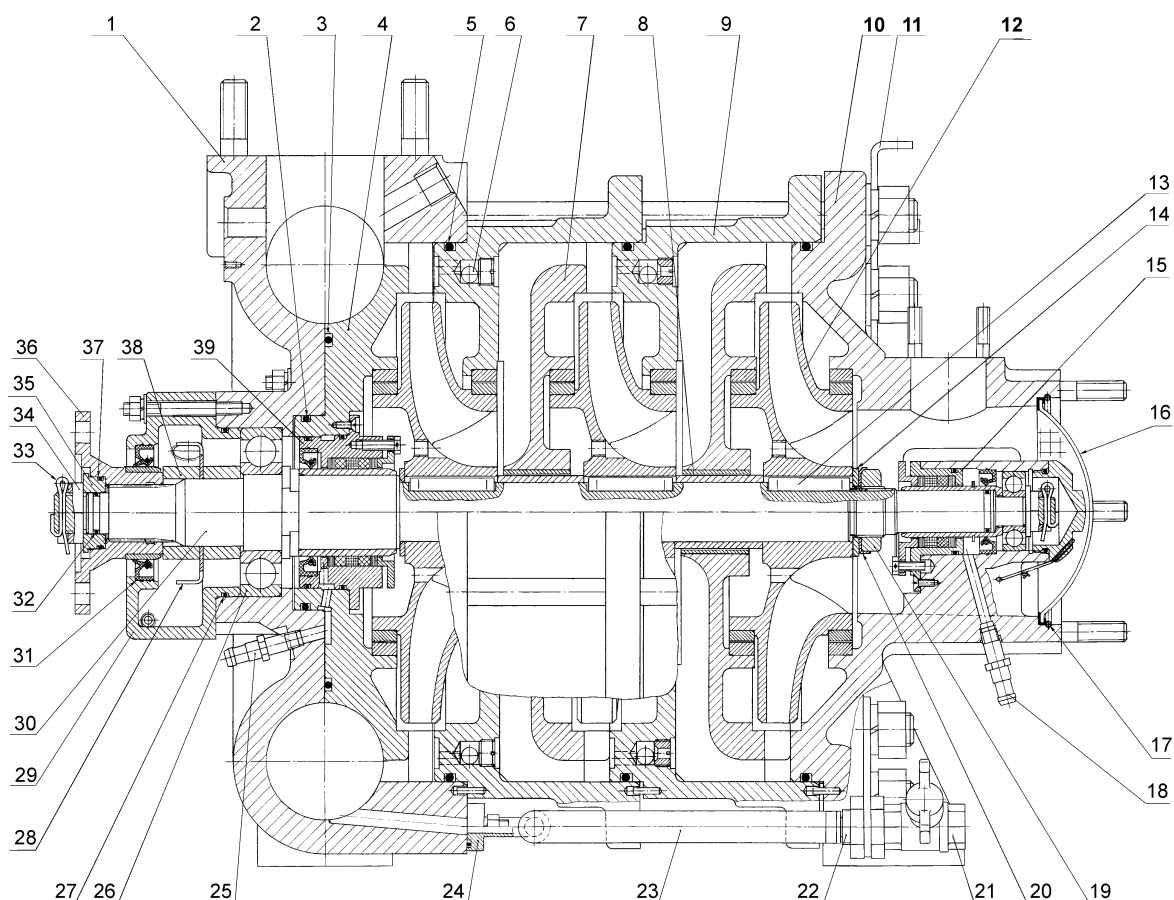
Насос центробежный (разрез по оси ротора): 1 – корпус; 4 – аппарат направляющий третьей ступени; 6 – клапан; 7 – аппарат
